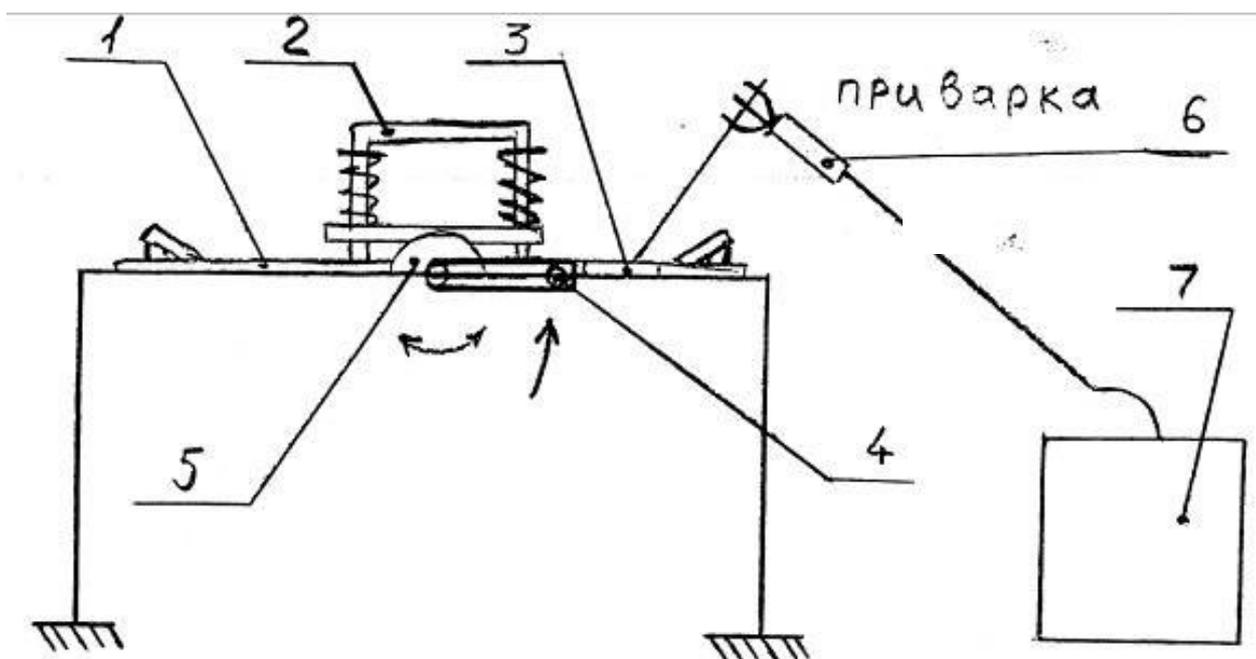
Схема приспособления для сварки лезвий:
